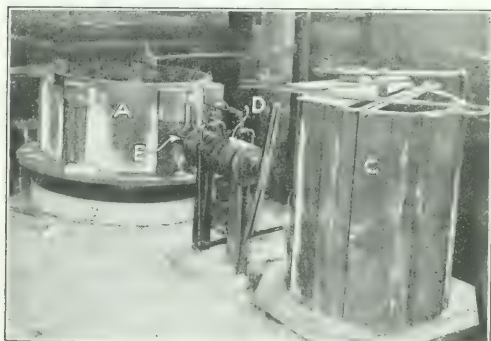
CARRETAS PARA MANDRILES DE RELLENAR CON BABBITT
